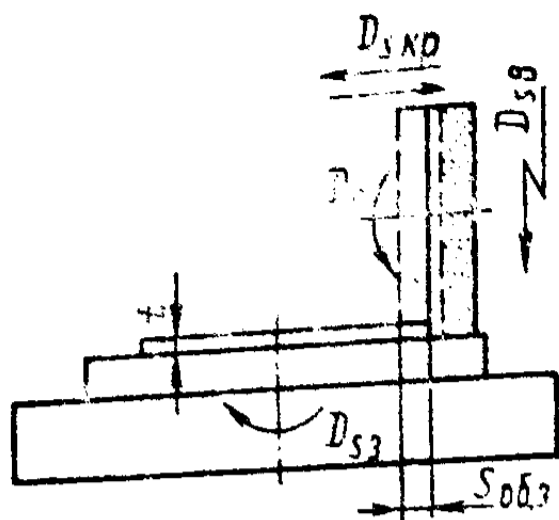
Схема обработки заготовок периферией круга на плоскошлифовальном станке с круглым столом
